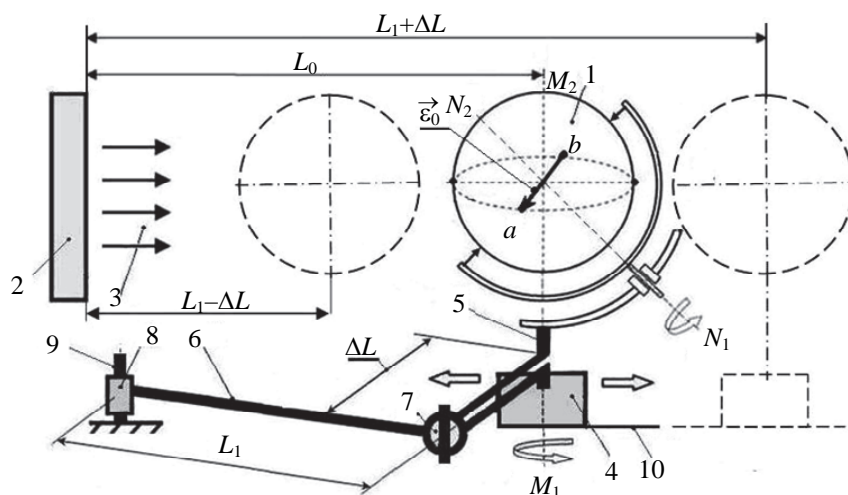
Схема устройства для напыления: 1 – сферический ротор; 2 – источник напыляемого материала; 3 – поток напыляемого материала; 4 – привод вращения ротора 1 вокруг основной оси M_1M_2 ; 5 – одноколенный вал; 6 – шатун; 7, 8 – шарниры; 9 – упор; 10 – направляющая
